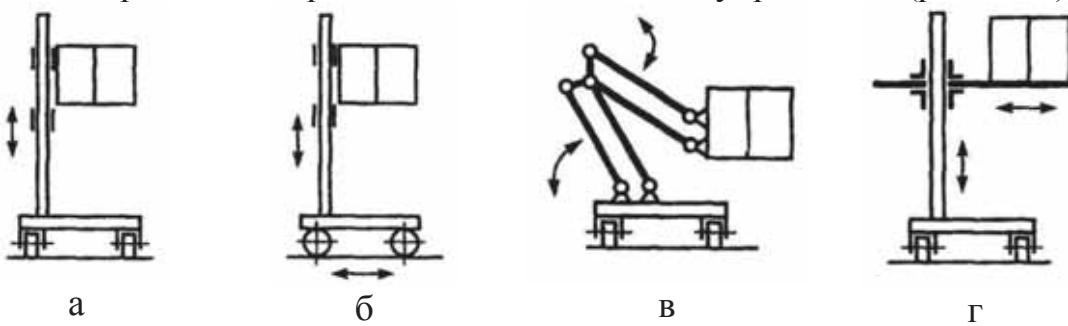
Передвижные площадки для сварщика: а – с передвижением вдоль фронта работ; б – с передвижением поперек фронта работ; в – шарнирно-рычажная; г – координатная
